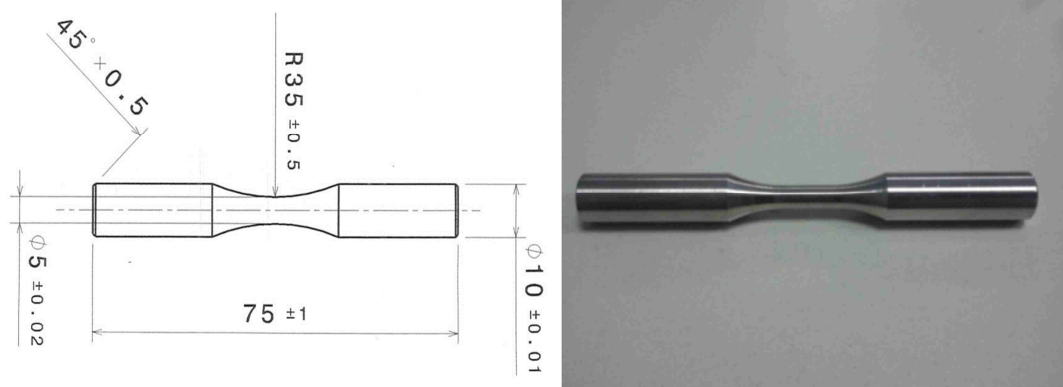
Dimensions (en mm) de l'éprouvette de fatigue destinée aux tests de fatigue en flexion rotative.
